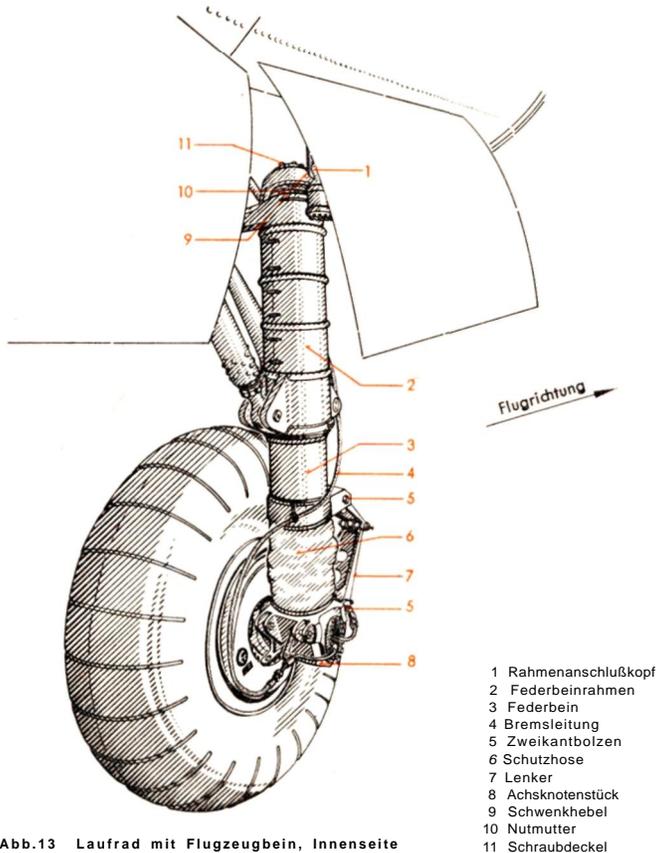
Laufrad mit Flugzeugbein, Innenseite
